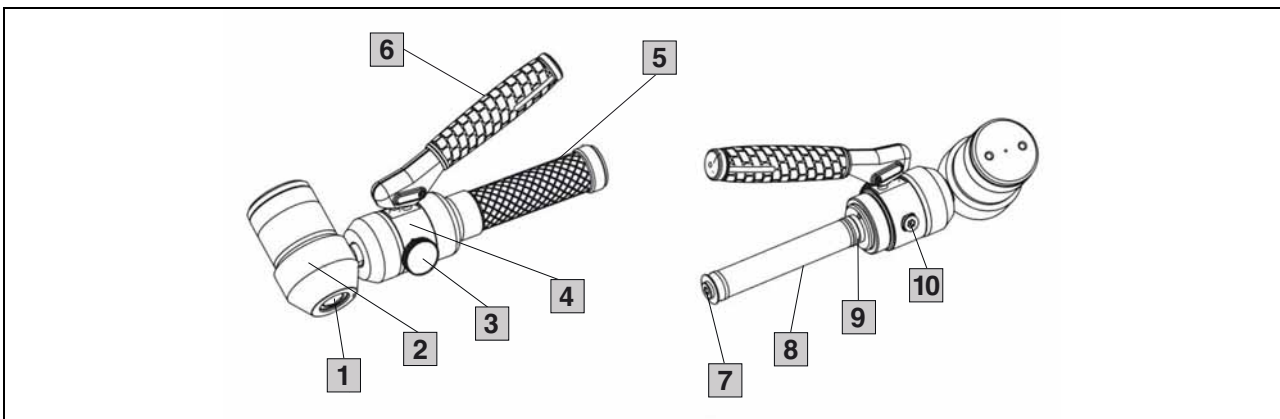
Hand-Hydraulikstanze mit 90° abgewinkeltem und 360° drehbarem Zylinderkopf/
